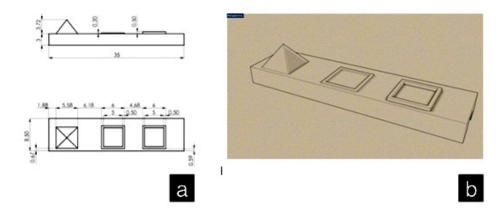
(a) Imagen del plano de la Pieza 2.1 con dimensiones de la plantilla longitudinal, en la que se aprecia su geometría en planta y alzado; (b) vista de la pieza en perspectiva correspondiente al archivo en formato STL para imprimir
